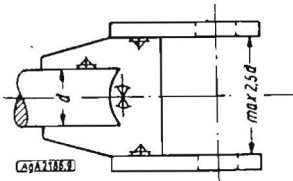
Geschmiedete oder Stahl-Gelenkgabel. Diese ist für Stumpfschweißung (Abbrennschweißung) besonders geeignet. Bei Anwendung der Schmelzschweißung muß die X-Naht angewendet werden
